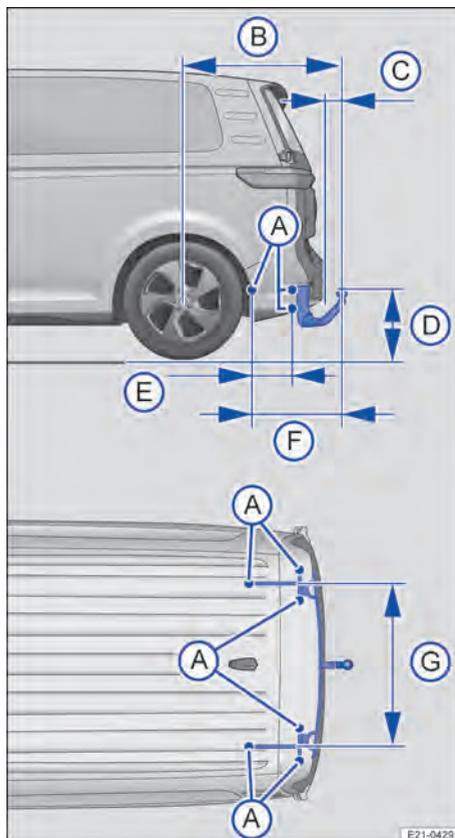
Pontos de fixação para a instalação posterior de um dispositivo de reboque.
